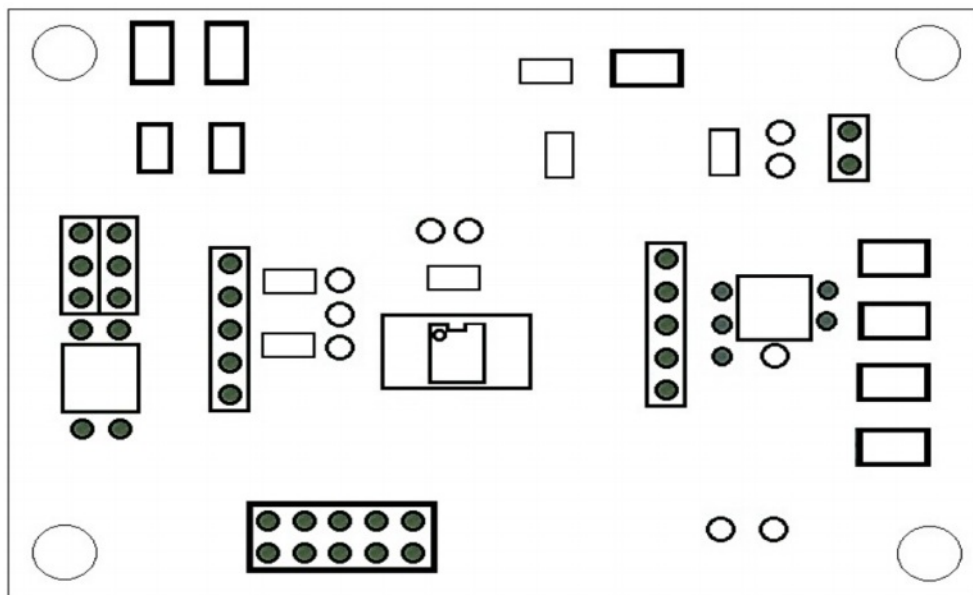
MOTOR CONTROLLER BOARD 부품배치도
